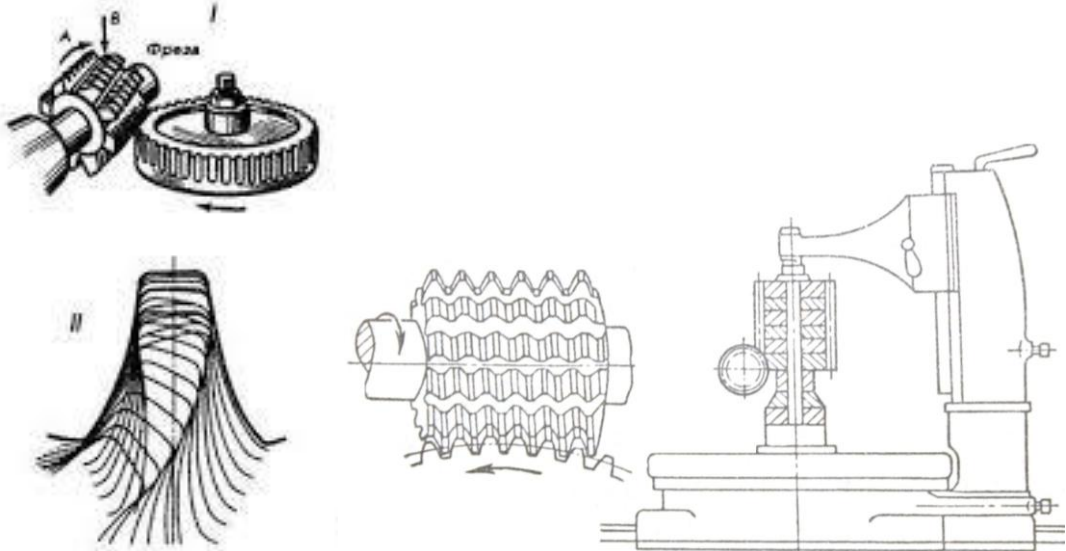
Схема обработки цилиндрических зубчатых колес
